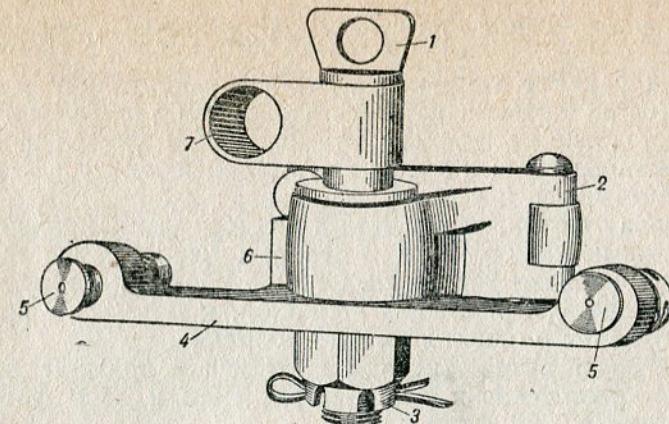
Кронштейн для крепления фотокинопулемета на истребительном самолете (вид сверху)
